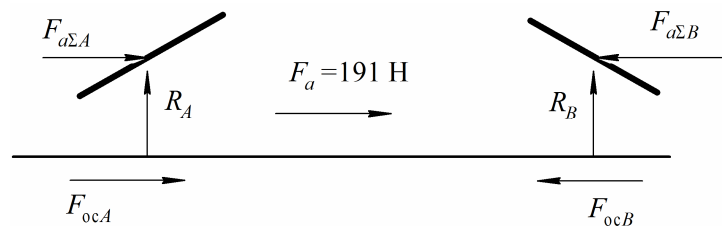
Схема нагружения промежуточного вала и подшипников
